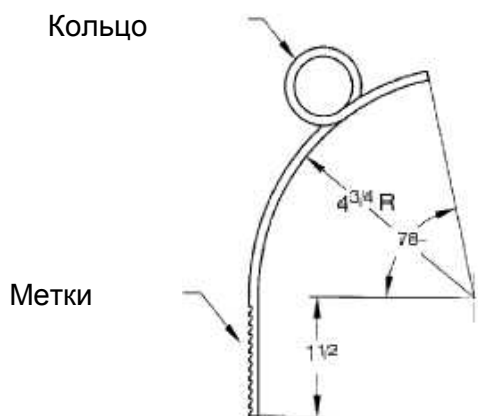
Измерительный Щуп для Компрессора York 210
